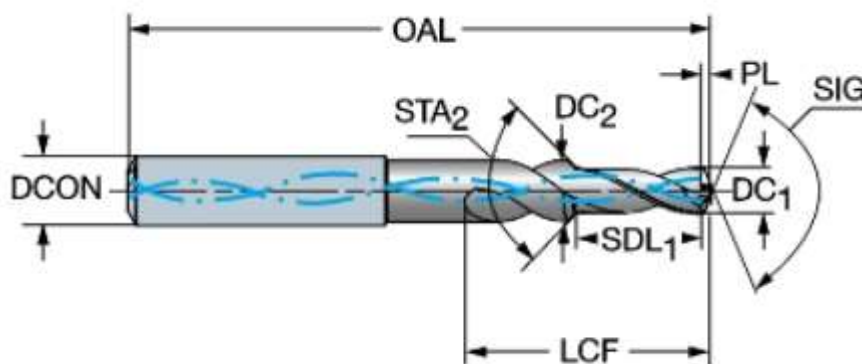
Свердло фірми Sandvik(460.2-0690-021A1-XM GC34) [8]
